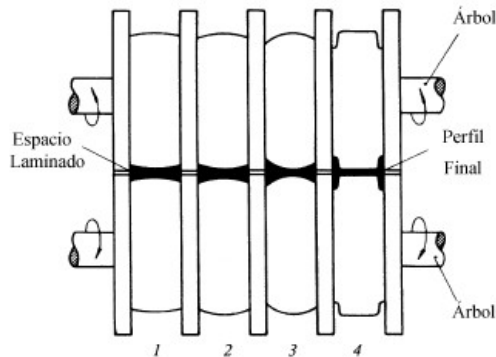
Esquema de máquina laminadora. Fuente: Hidalgo de Caviedes, 1975.
